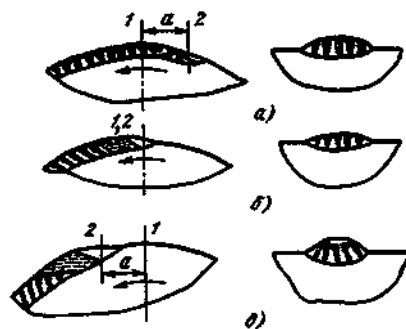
Вплив величини зміщення електроду від zenіту на формування валика наплавленого металу (напрямок обертання зазначений стрілкою)
